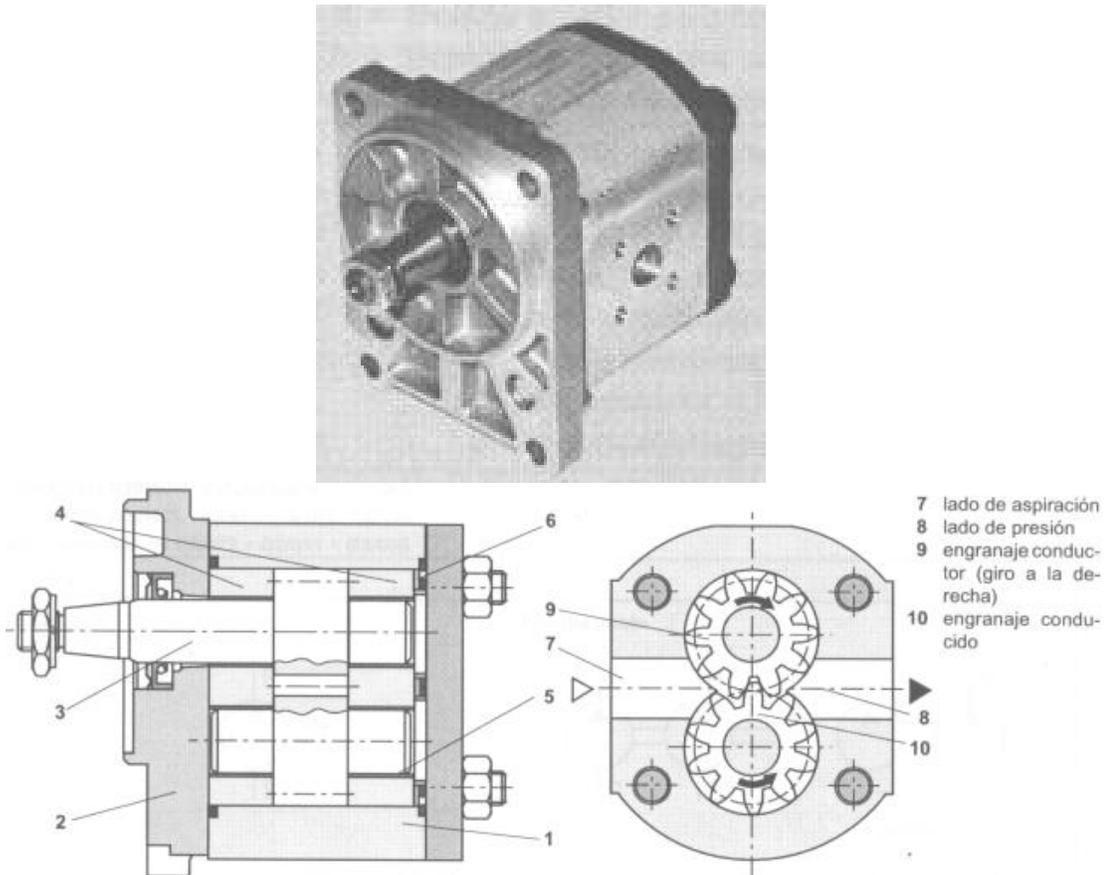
Bomba Parte Central: Engranajes, Caudal Constante
